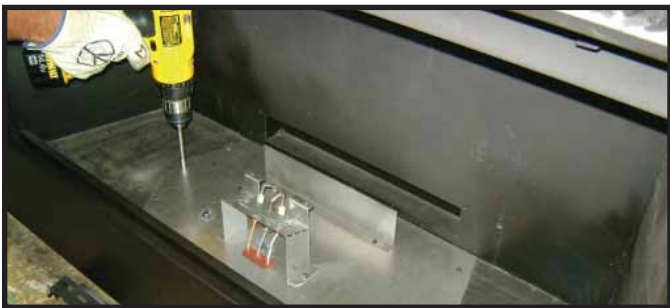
Entfernen der Ventilplattenschrauben
